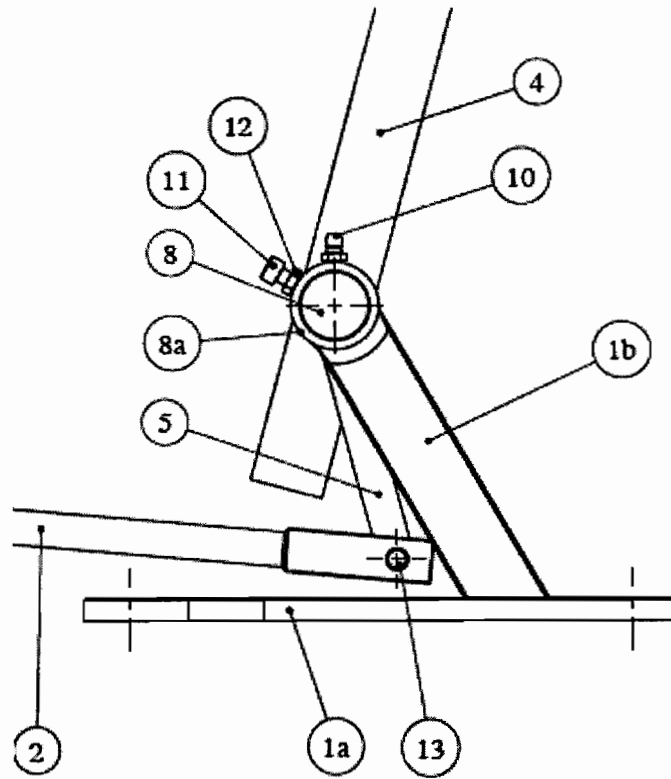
Elemente componente suport de fixare și lagăr – vedere laterală
